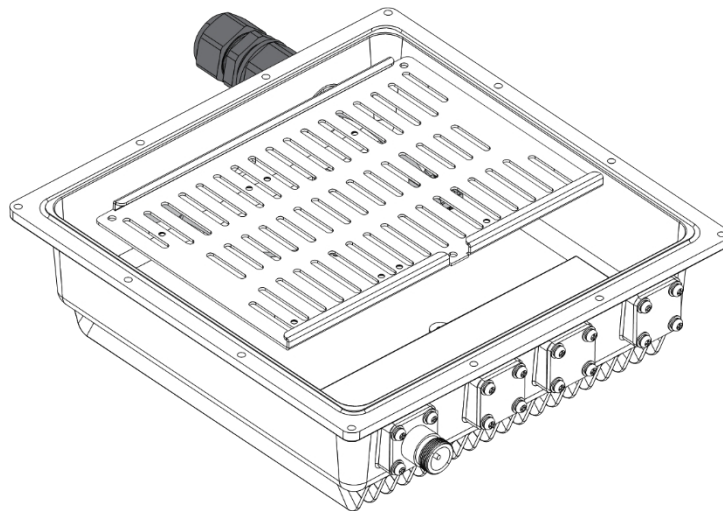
□ Montageplatte im Inneren des RAKBox-GW-3-Gehäuses
